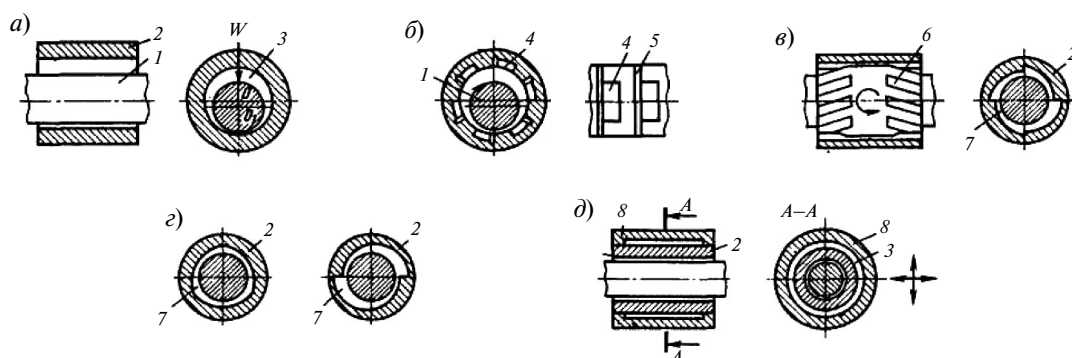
Газодинамический радиальный подшипник с жесткими рабочими поверхностями трения:
